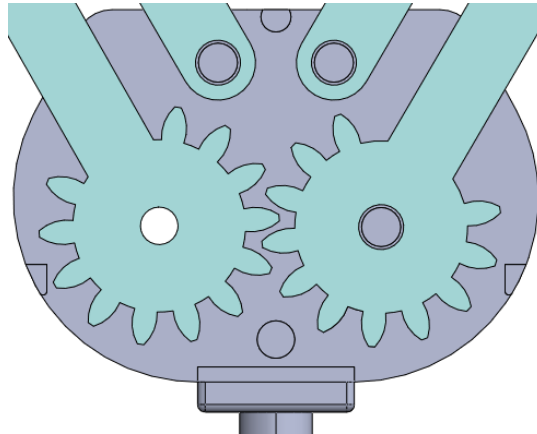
Garra com desvio de engrenagem para impressão 3D
